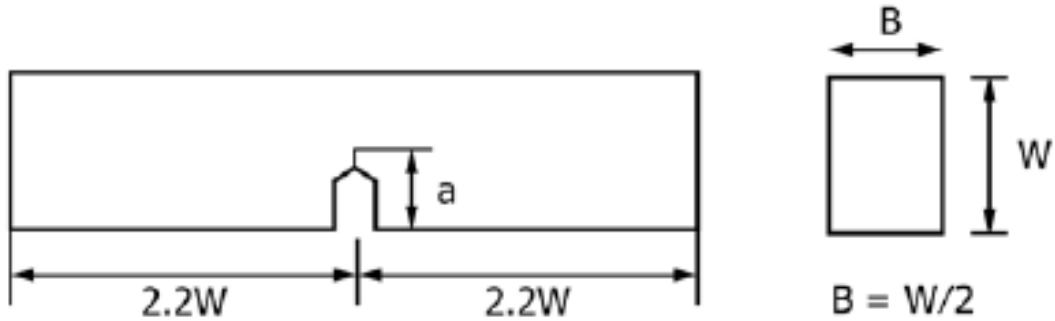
Geometría de probetas para ensayos. Fuente: ASTM D5045-14.
